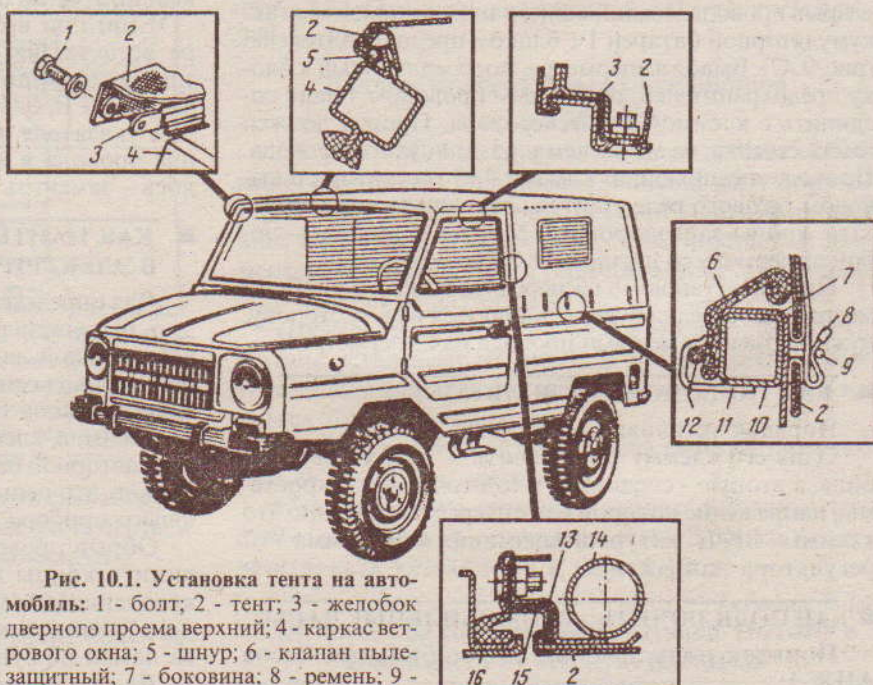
Установка тента на автомобиль: 1 - болт; 2 - тент; 3 - желобок дверного проема верхний; 4 - каркас ветрового окна; 5 - шнур; 6 - клапан пылезащитный; 7 - боковина; 8 - ремень; 9 - скоба; 10 - каркас боковины; 11 - скоба; 12 - прижим; 13 - желобок дверного проема; 14 - дуга безопасности передняя; 15 - прижим дверного проема боковой; 16 -
